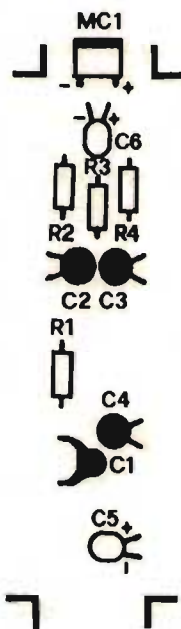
Circuito stampato cod. 890.66: montaggio dei componenti (lato B).
